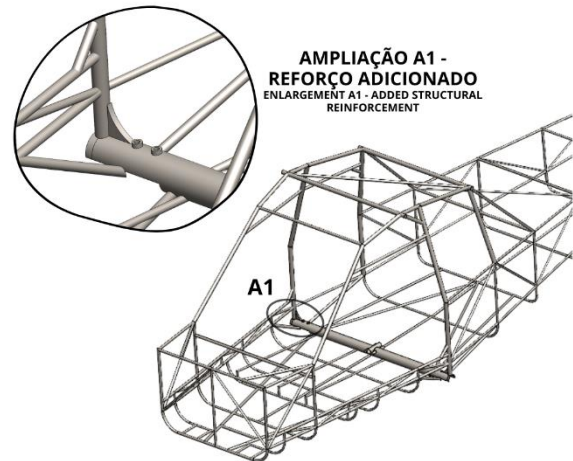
Desenho técnico do local de aplicação do reforço estrutural
